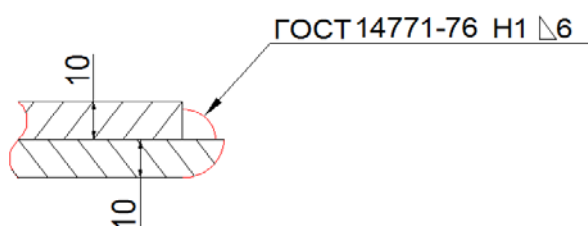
Схема сварного соединения Н1 по ГОСТ 5264-80 [12]
